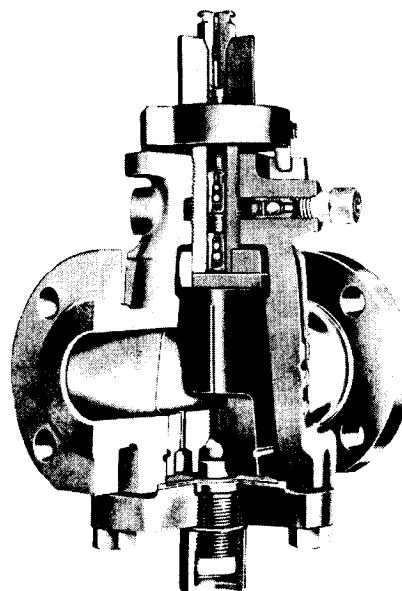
Válvula de macho lubricada; tapa inferior atornillada
